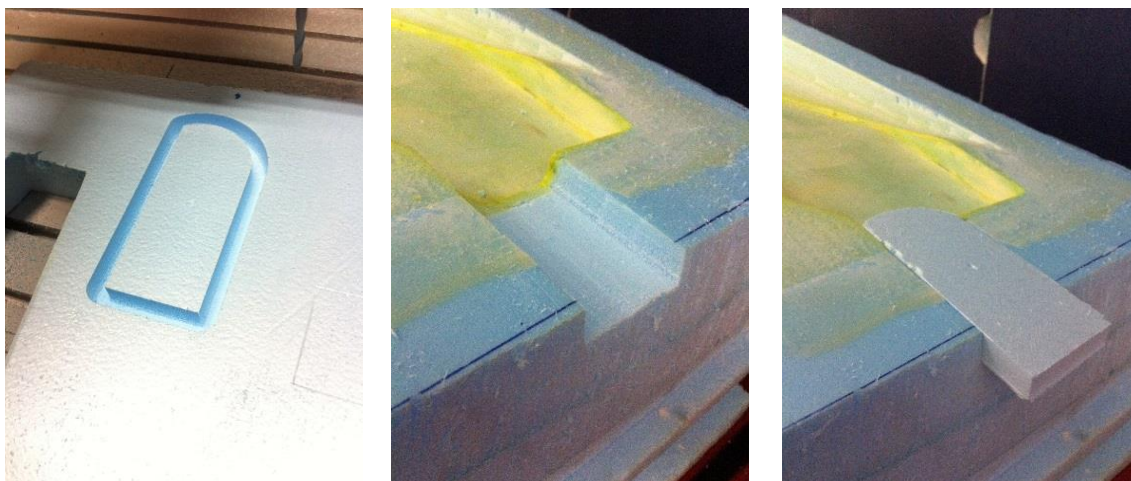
Maquinação do molde macho e inserção na abertura destinada ao efeito.
